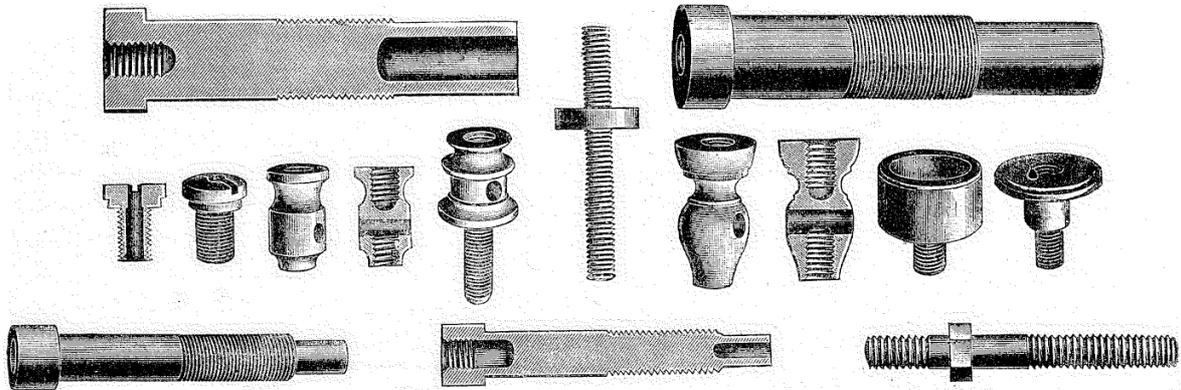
Travaux exécutés avec la machine à vis Spencer.
